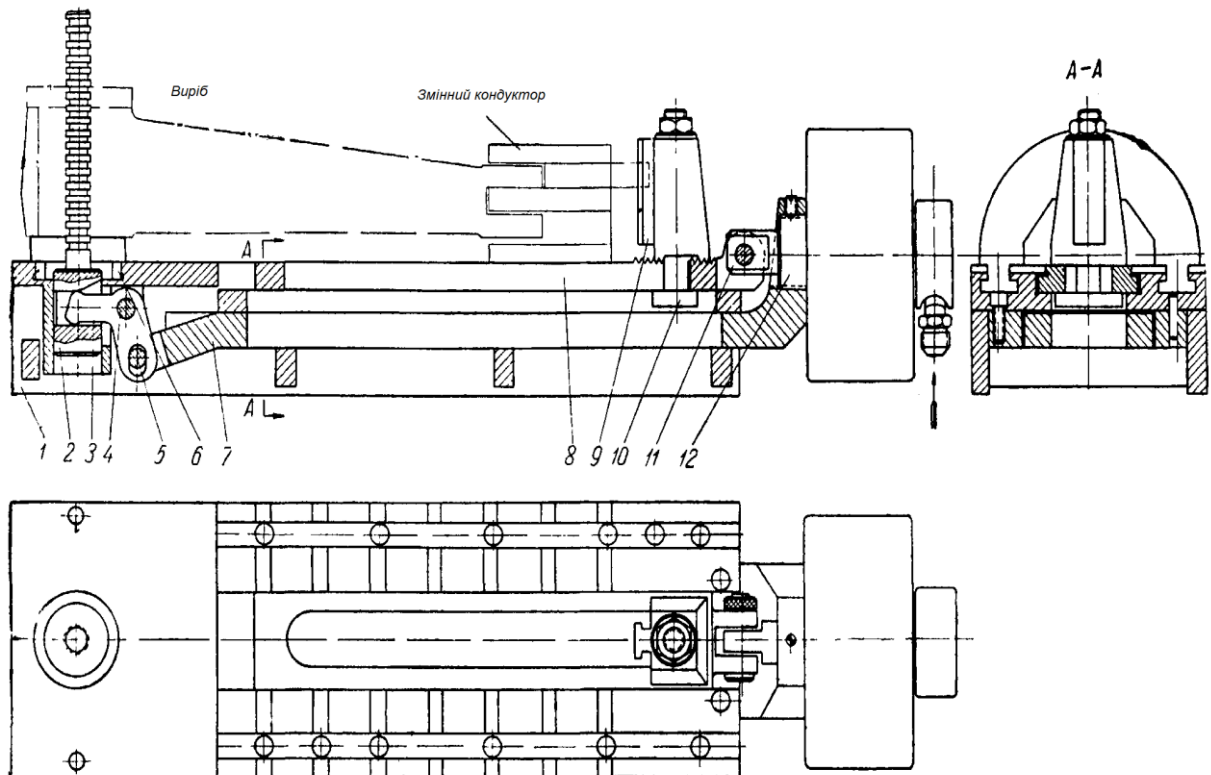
Універсальний корпус для свердління важелів і вилок
